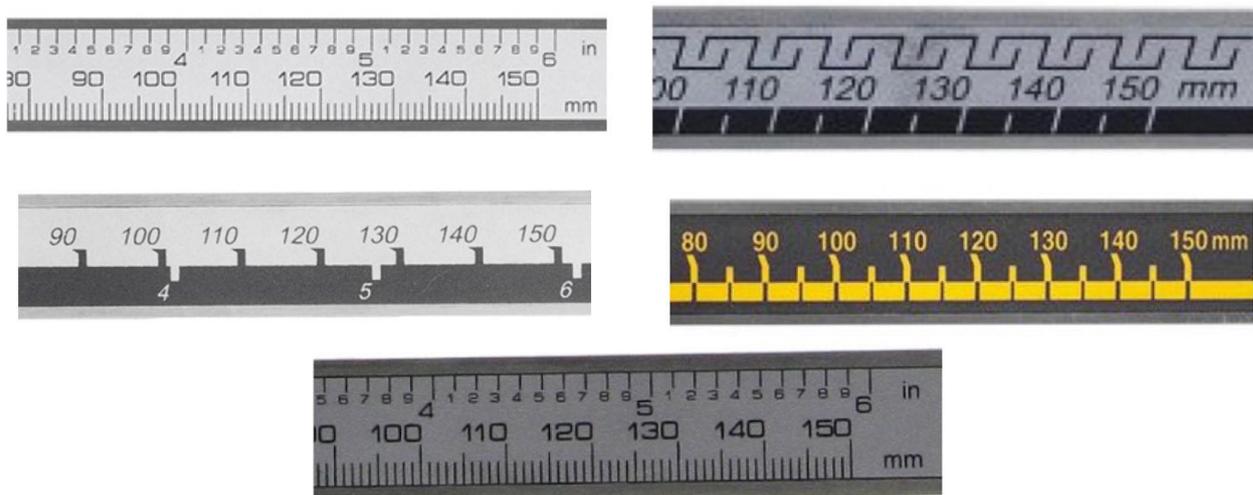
Внешний вид штанги штангенглубиномеров
